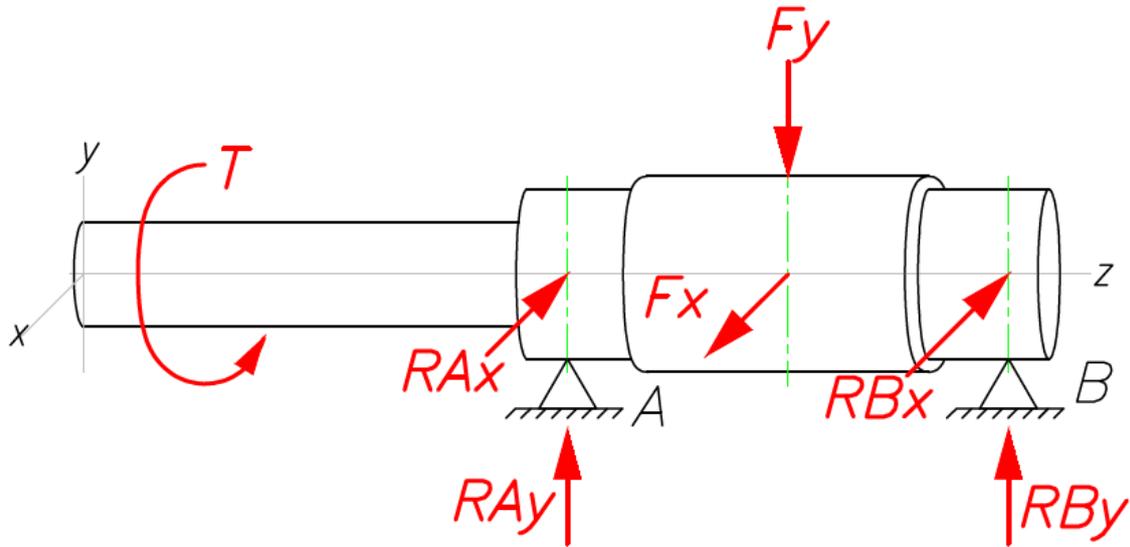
DCL eje proyectado. Fuente: (Autor)
